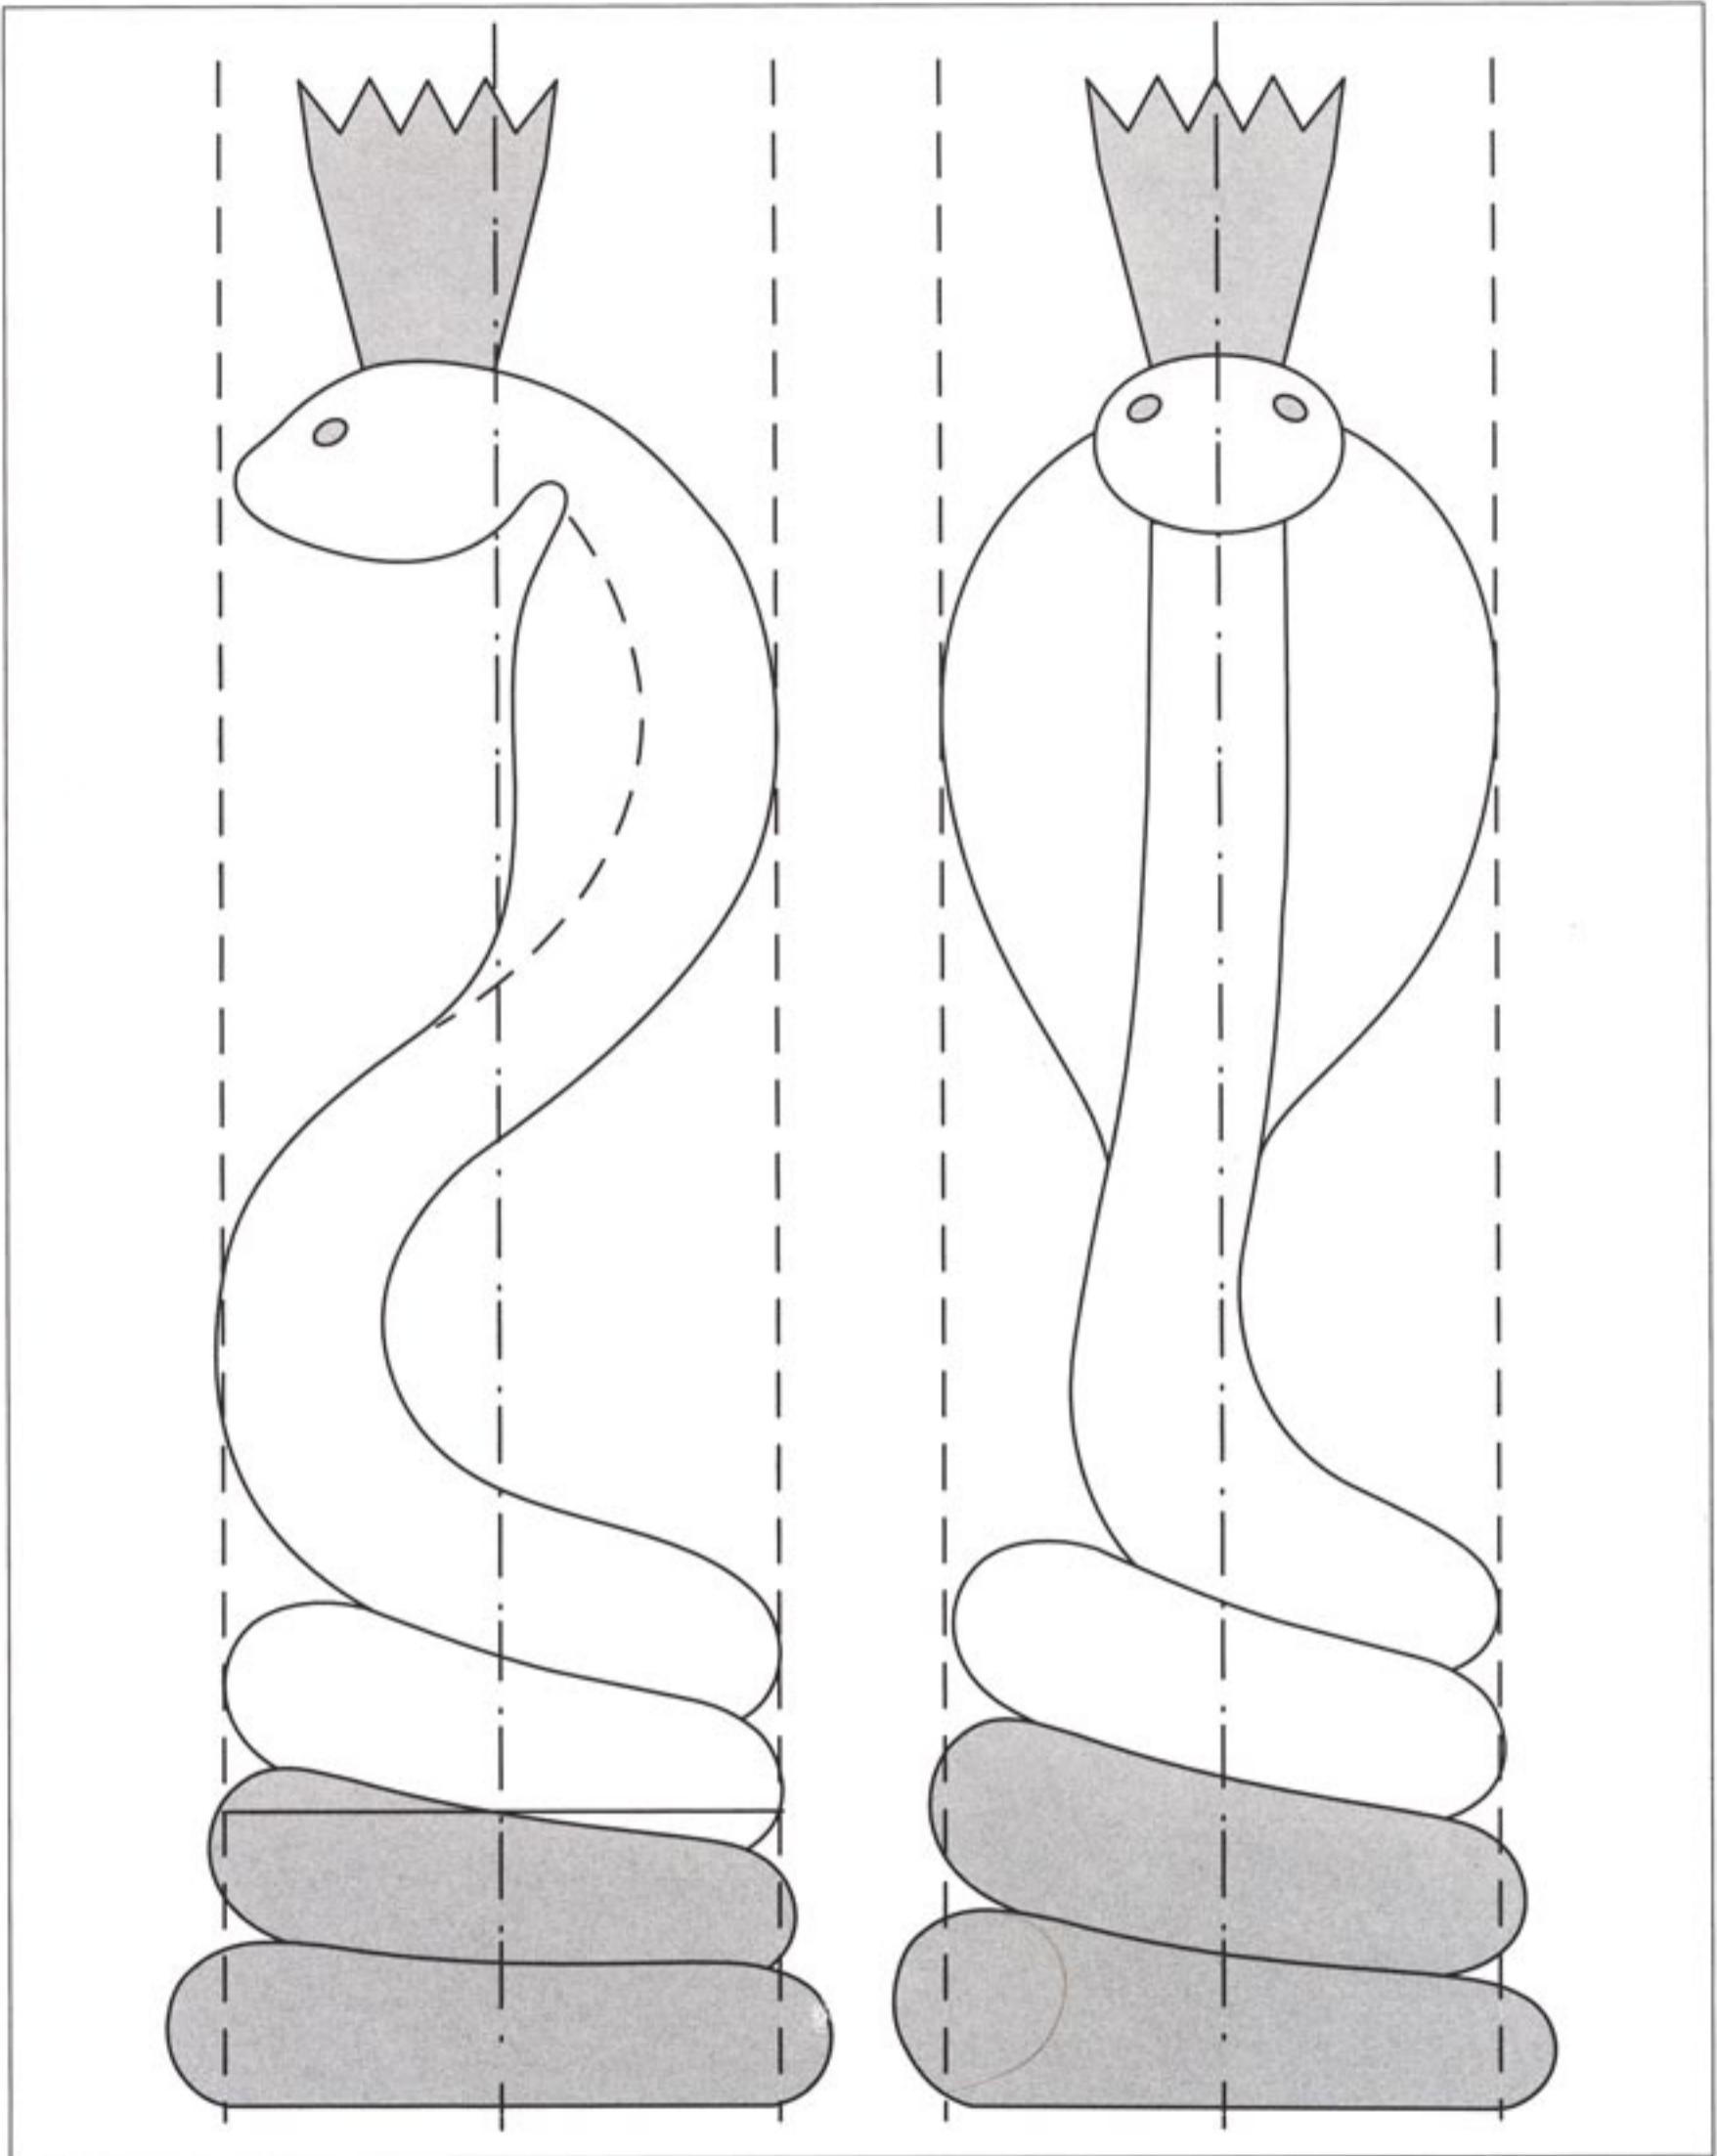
Чертеж и схема стойки и основания стилизованного подсвечника "Кобра" к рис. 190. Размеры заготовки: длина – 25 см; диаметр – 8 см. Диаметр заготовки для основания, которое подклеивают к стойке снизу – 12–14 см
